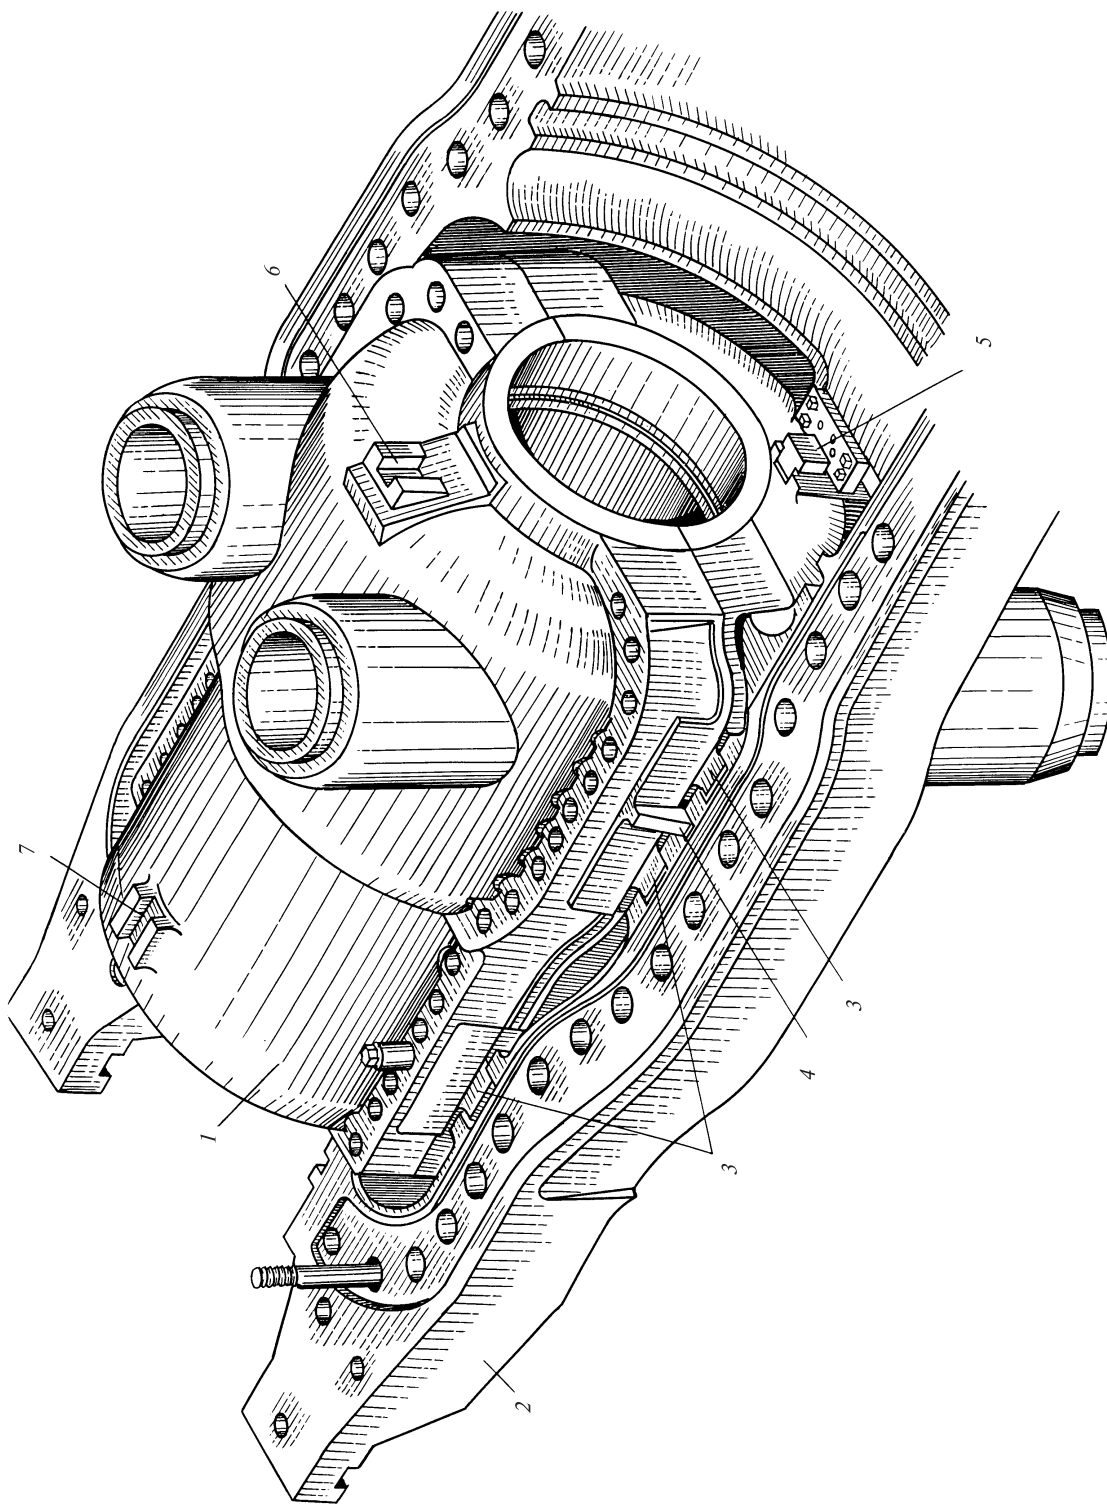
Установка внутреннего корпуса двухстороннего цилиндра во внешнем корпусе
